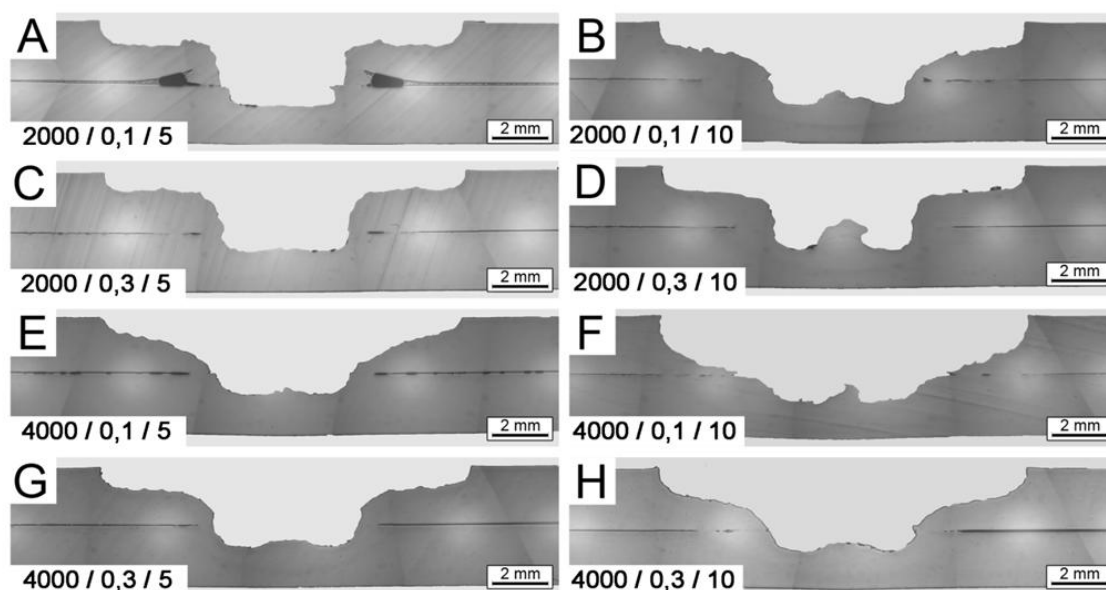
Seção transversal das amostras de PMMA soldadas por FSSW. Cada amostra representa uma das condições soldadas dentro do planejamento de experimentos.
